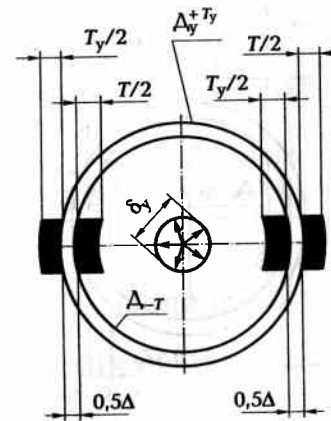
Схема установки цилиндрического вала в цилиндрическое отверстие установочного элемента приспособления
